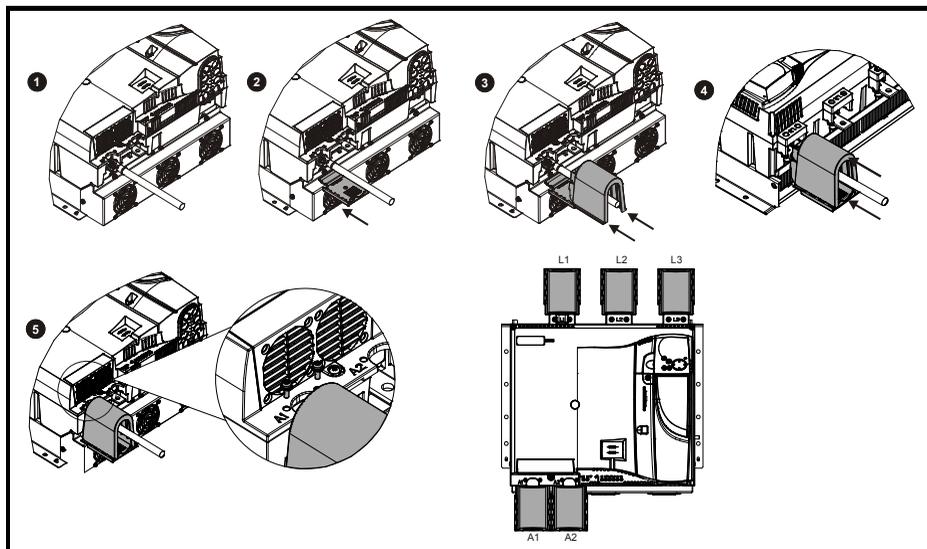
Extracción de las cubiertas de terminales de los accionamientos de tamaño 1
